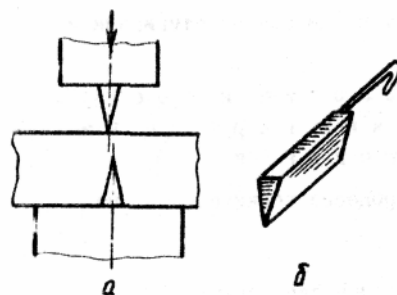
Схема отрубки (а) и инструмент для отрубки (б)
